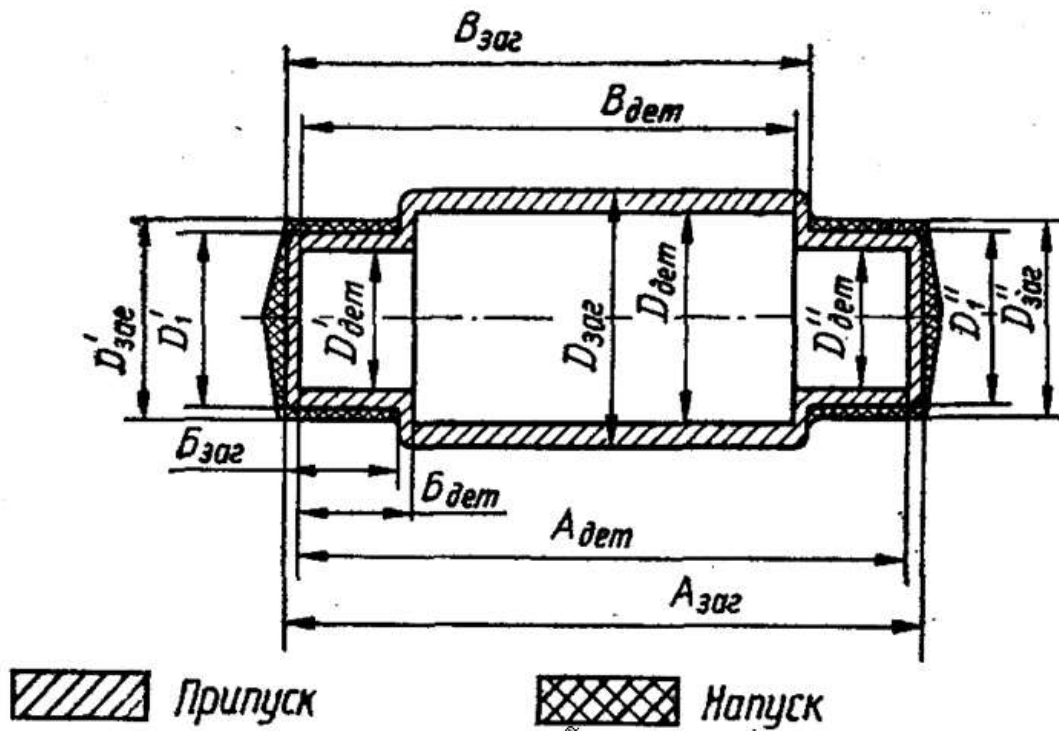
Припуски, напуски і розміри вала [3]:
